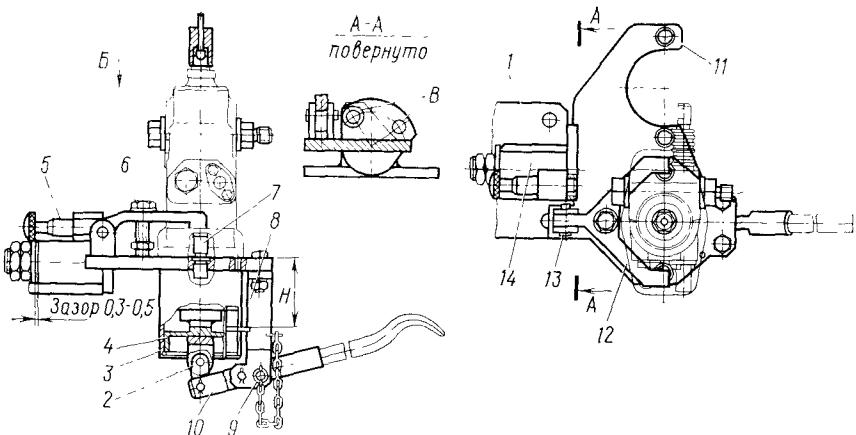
Приспособление для обслуживания топливного насоса высокого давления:
